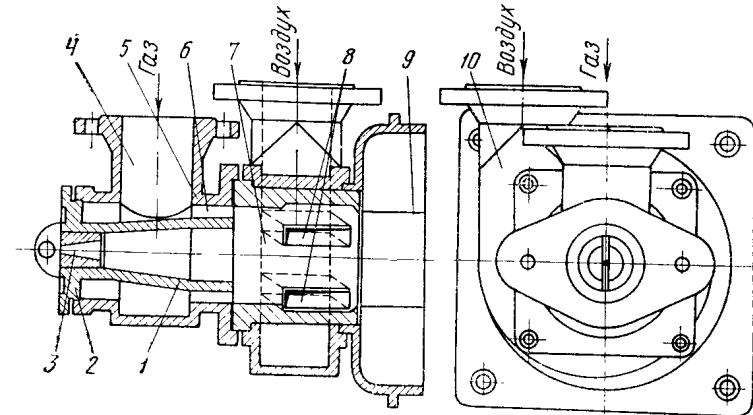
Газовая горелка низкого давления конструкции Стальпроекта:
